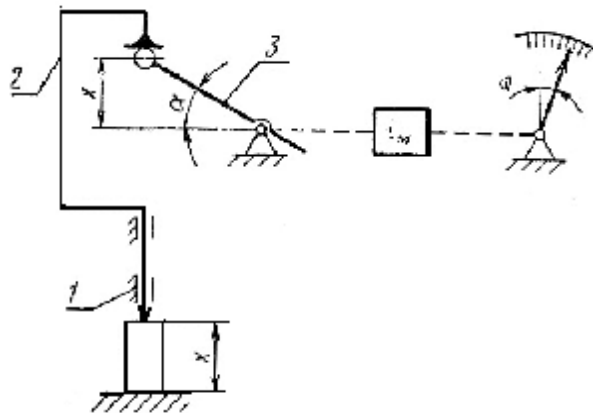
Схема измерительной цепи с синусной рычажной передачей: 1 – корпус; 2 – измерительный стержень; 3 – ведущее плечо рычага
